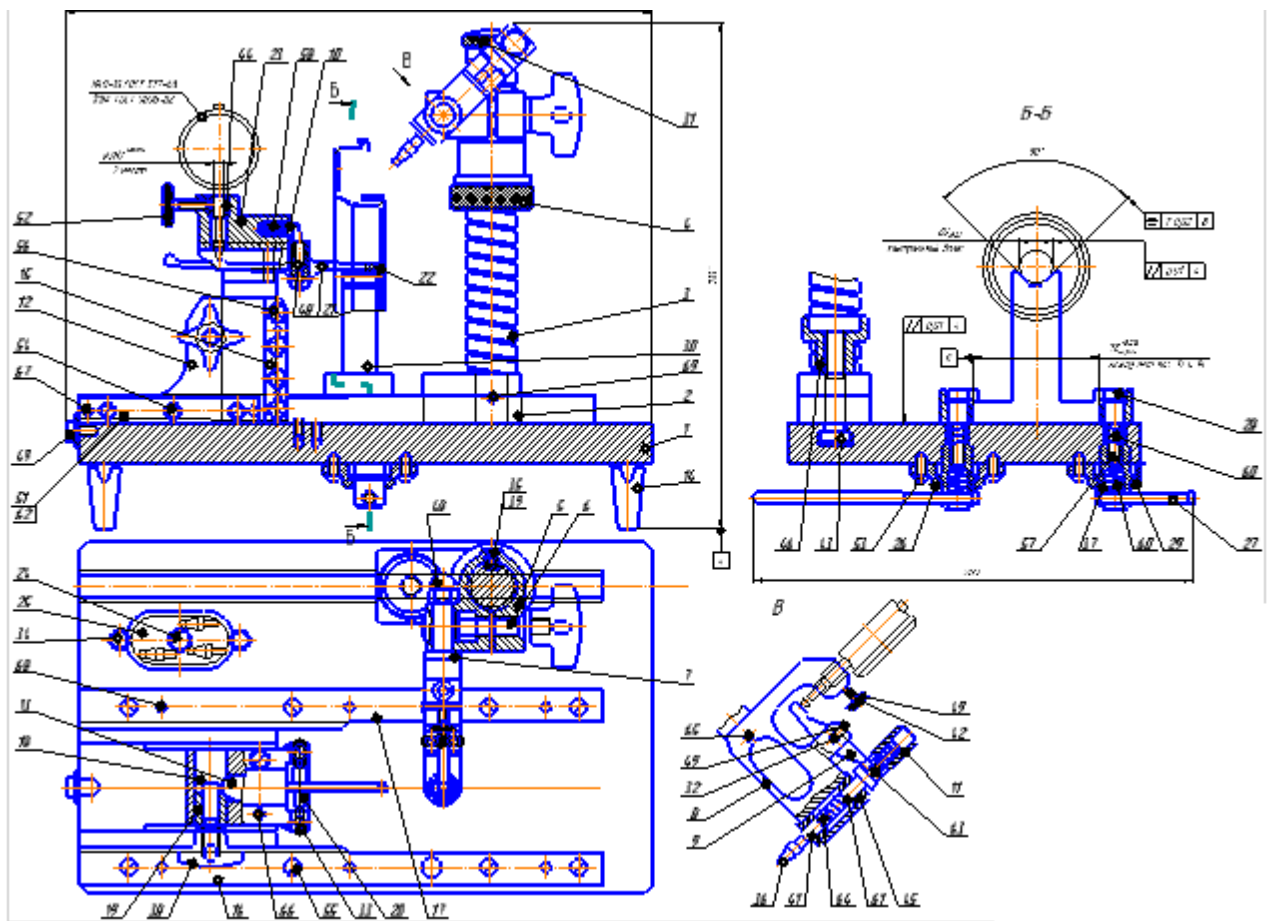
Ескіз для контролю розмірів деталі
